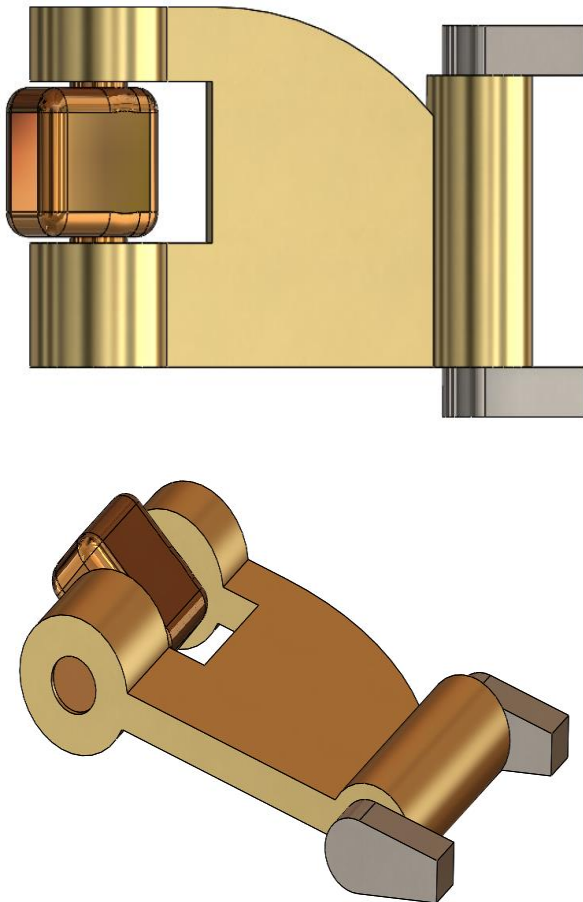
Ensamblaje de Componentes en vista Superior e Isométrica
